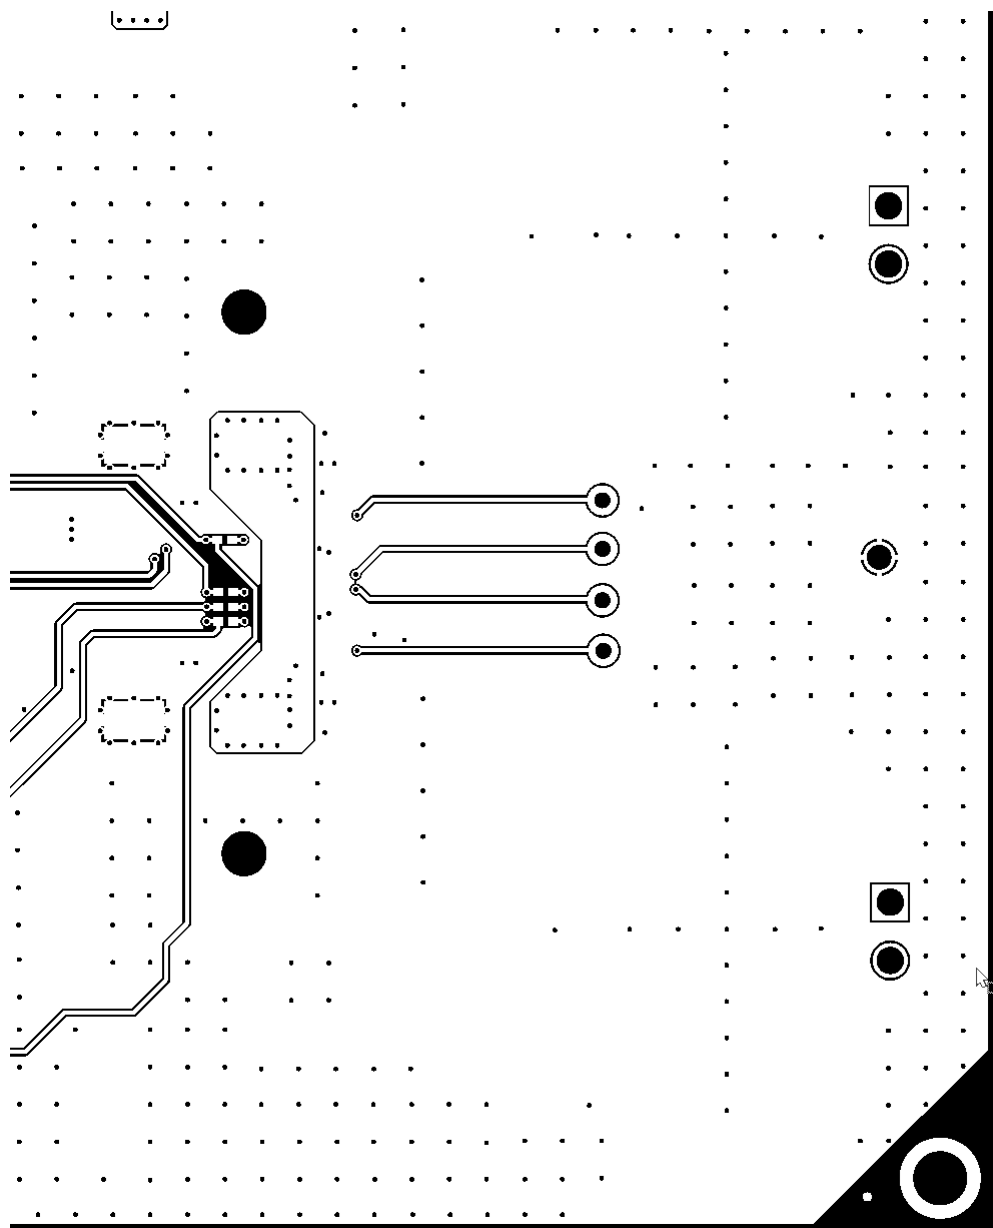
2.0 (立体声 BTL) PCB 低层图 (顶视图)
